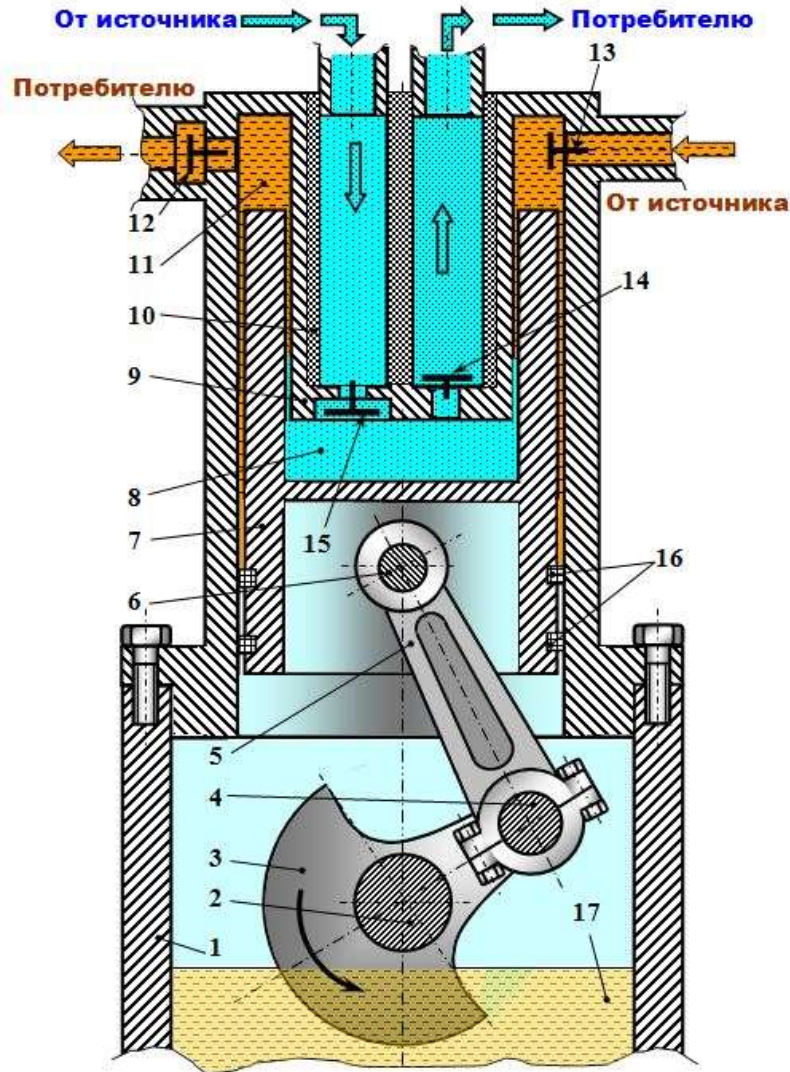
Схема бескрейцкопфной поршневой гибридной энергетической машины улучшенной конструкции: 1 – картер; 2 – коленчатый вал; 3 – противовес; 4 – кривошип; 5 – шатун; 6 – палец шатуна; 7 – тронковый поршень; 8 – компрессорная полость; 9 – выступ; 10 – теплоизоляция; 11 – насосная полость; 12 – нагнетательный клапан; 13 – всасывающий клапан; 14 – нагнетательный клапан; 15 – всасывающий клапан; 16 – уплотнение; 17 – масло
